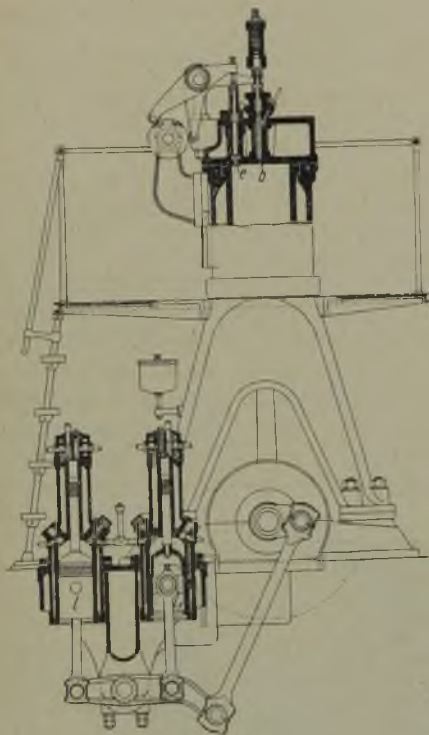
Seitenansicht des Dieselmotors sowie Schnitt durch einen Zylinder und die Luftpumpen.
